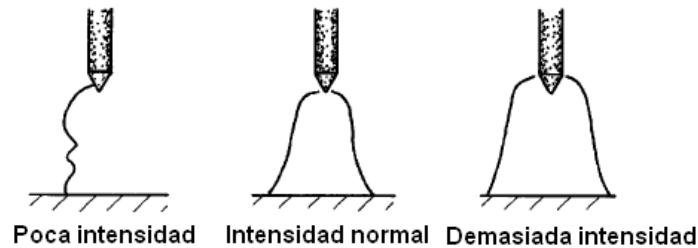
Formas de arco para soldadura TIG, en función de la intensidad.
